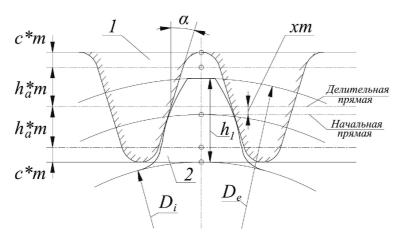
Схема для определения коэффициента радиального смещения х инструмента: 1 — исходный производящий контур (ИПК) режущего инструмента; 2 — заготовка
